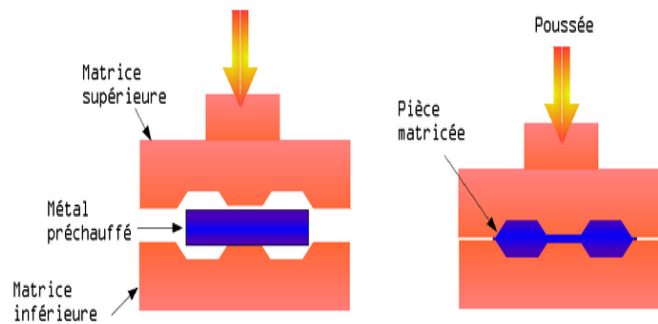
Schéma d'élaboration par forgeage (pièces forgées).
